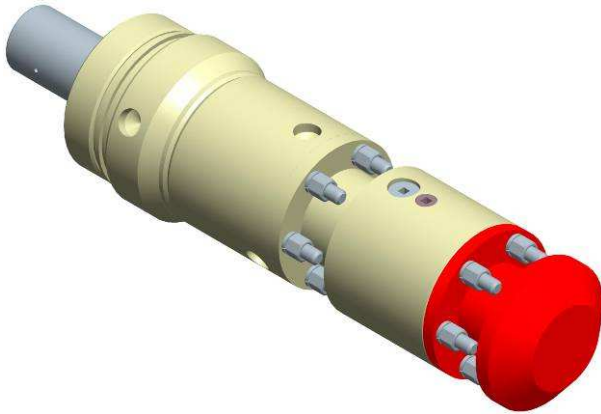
Внешний вид опоры подшипника ОП-117А
